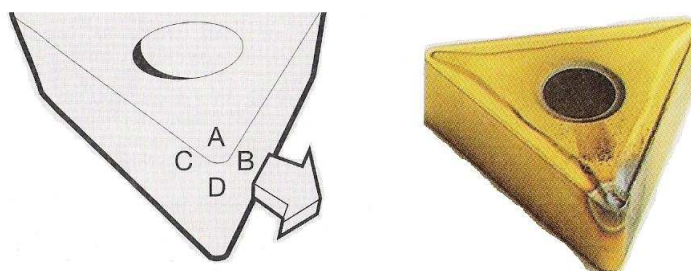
Diskrétní dotyk mezi řezným a obráběným materiálem [21]
